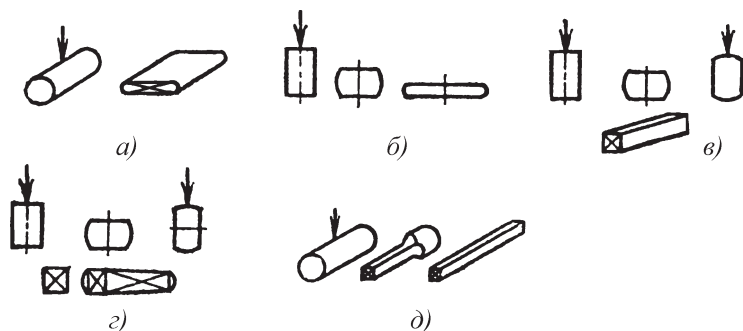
Схемы ковки заготовок из сплавов цветных металлов:
